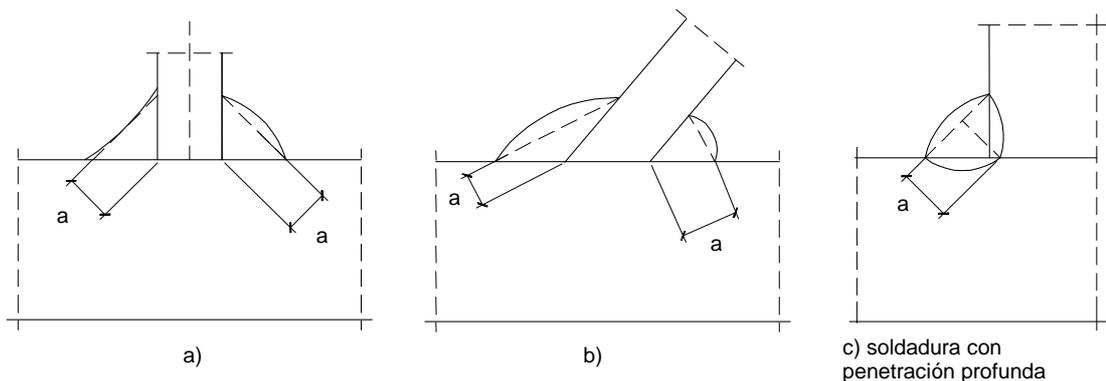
Soldadura en ángulo. Espesor de garganta
